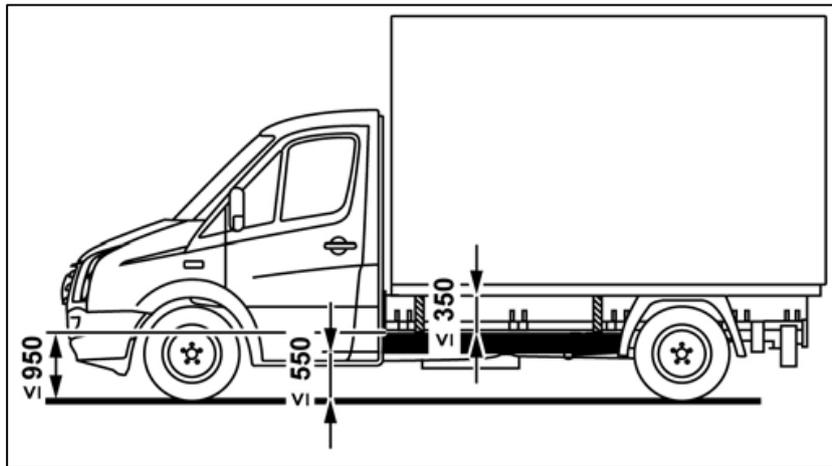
Positionnement du dispositif de protection latérale (schéma de principe)
